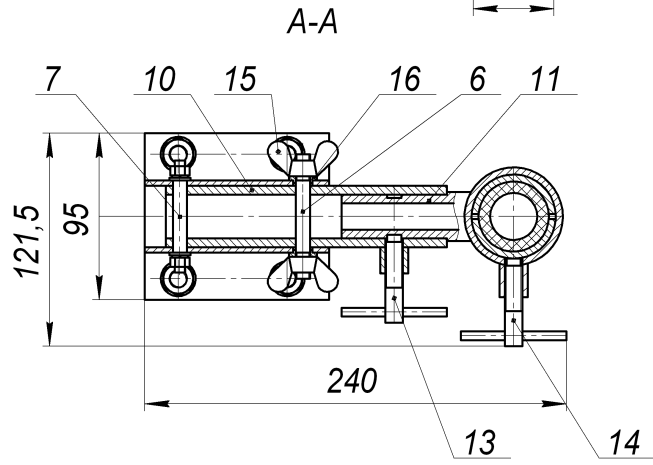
Ячейка калибровочная для поверки и регулировки погружных датчиков
